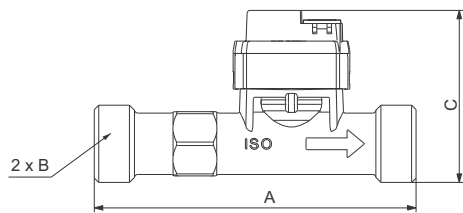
Abmessungen des Sensors MFS QT 4-40 l/min (mit Gewinde)
